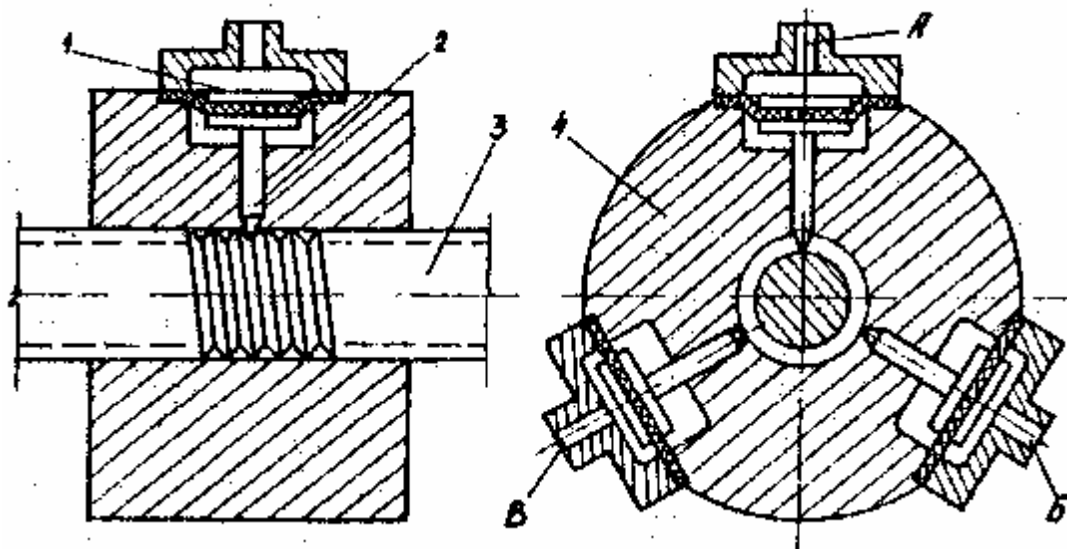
Трехтактный диафрагменный шаговый гидродвигатель кулачкового типа
